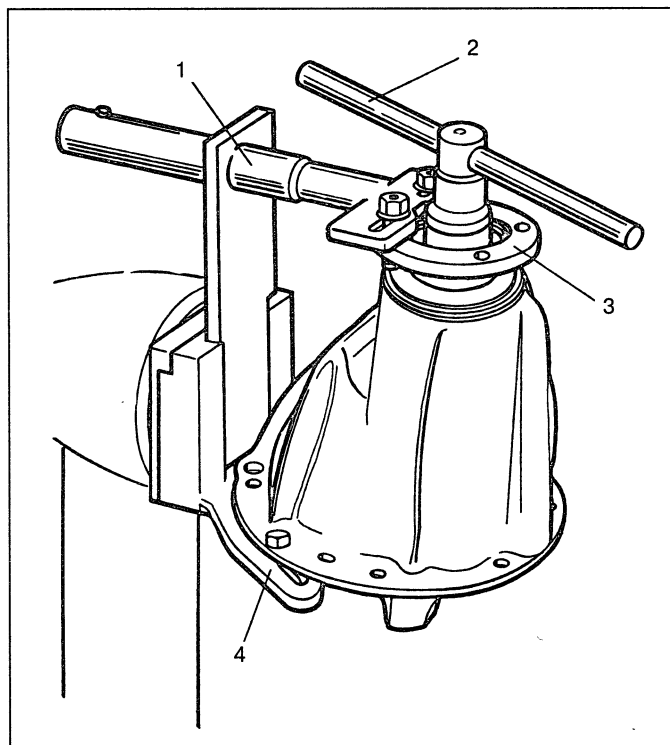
Отвертывание гайки ведущей шестерни: 1 – стопор для фиксирования фланца ведущей шестерни; 2 – торцевой ключ; 3 – фланец ведущей шестерни; 4 – кронштейн
